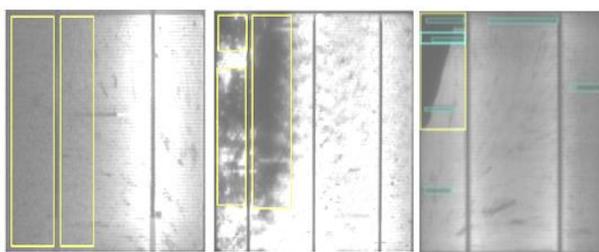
Imágenes de Electroluminiscencia de Módulos con manchas oscuras. a) Falla en soldadura, b) Defecto de celda, c) Rotura
